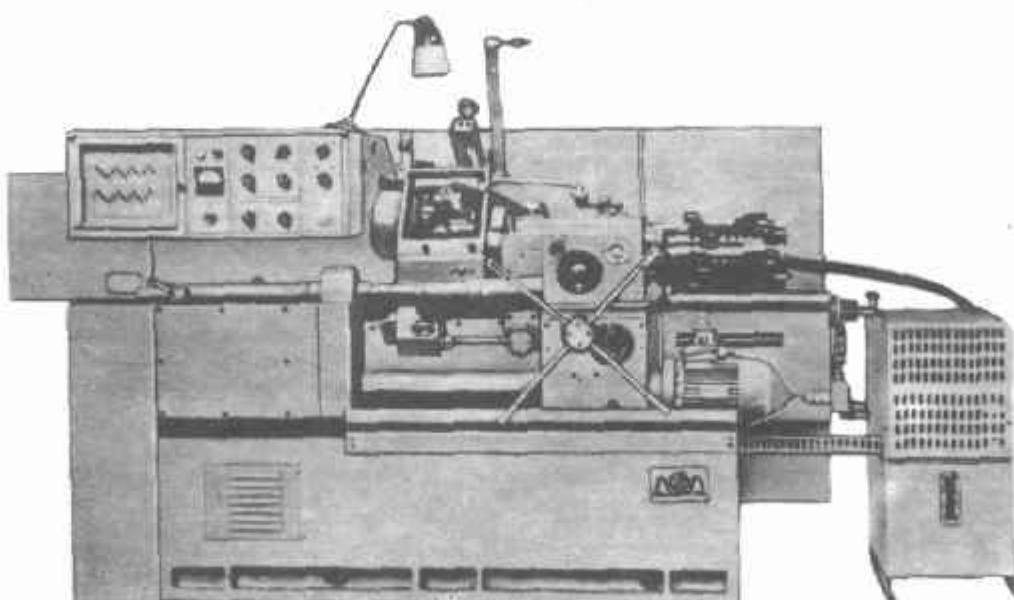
Токарно-револьверные станки 1Г340, 1Г340П
